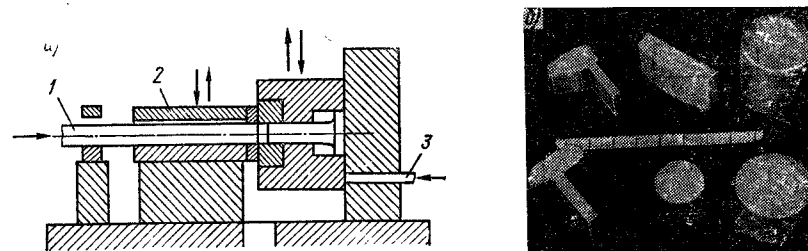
Схема чистой отрезки сдвигом (Венгерский патент): а -- схема установки; б — образцы профилей
